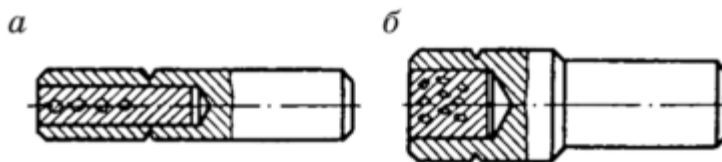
Алмазные карандаши с расположением алмазов: а — цепочкой; б — слоями
